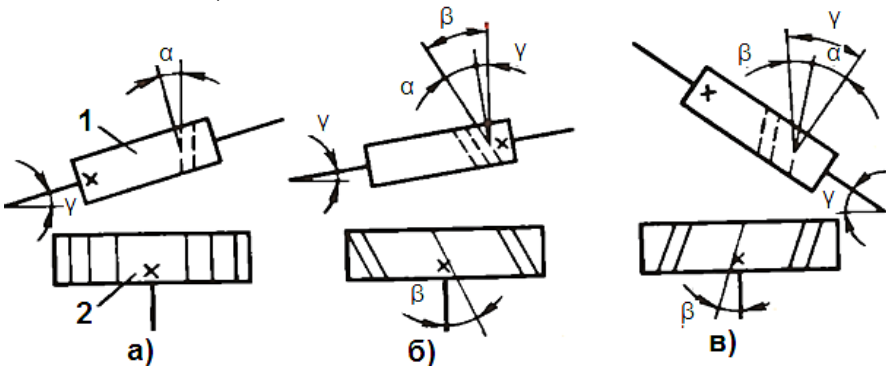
Схеми встановлення черв'ячної фрези для фрезерування циліндричних коліс
